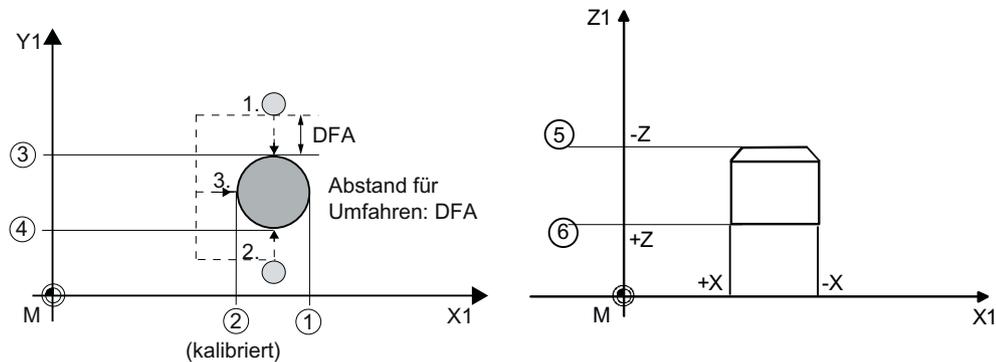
Werkzeugmesstaster Ausführung Scheibe und Würfel
